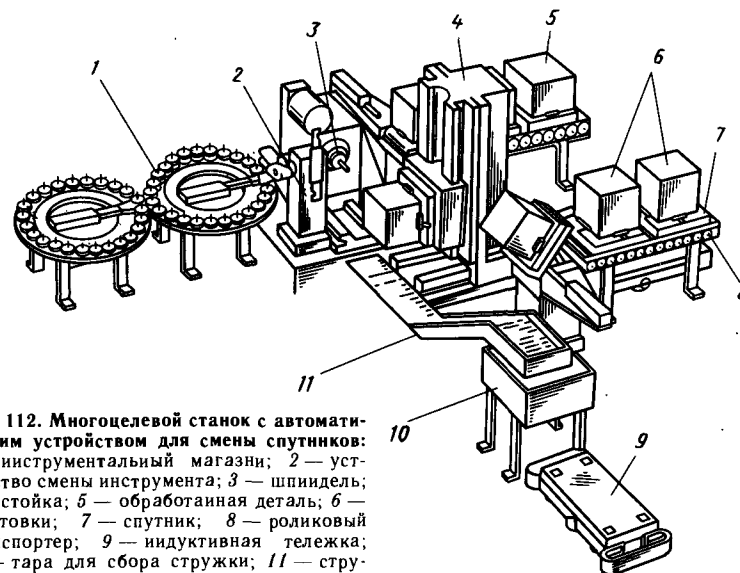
Многоцелевой станок с автоматическим устройством для смены спутников: 1 — инструментальный магазин; 2 — устройство смены инструмента; 3 — шпиндель; 4 — стойка; 5 — обработанная деталь; 6 — заготовки; 7 — спутник; 8 — роликовый транспортер; 9 — индуктивная тележка; 10 — тара для сбора стружки; 11 — стружечный транспортер
